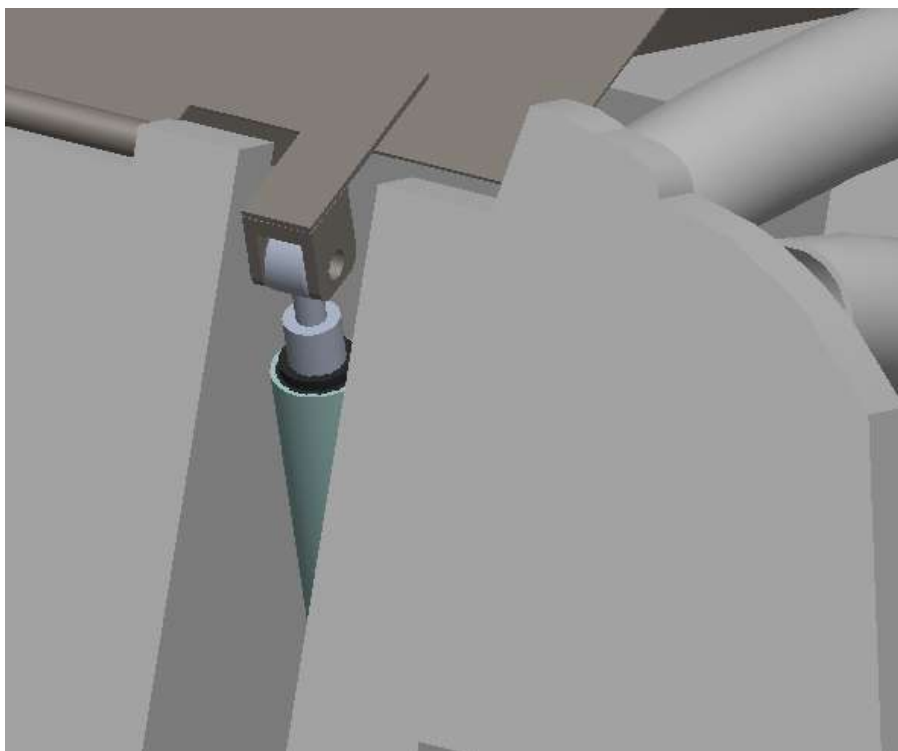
Sistema de apertura de puerta inferior con pistón de elevación. Fuente: (Vaca, José, 2018)
